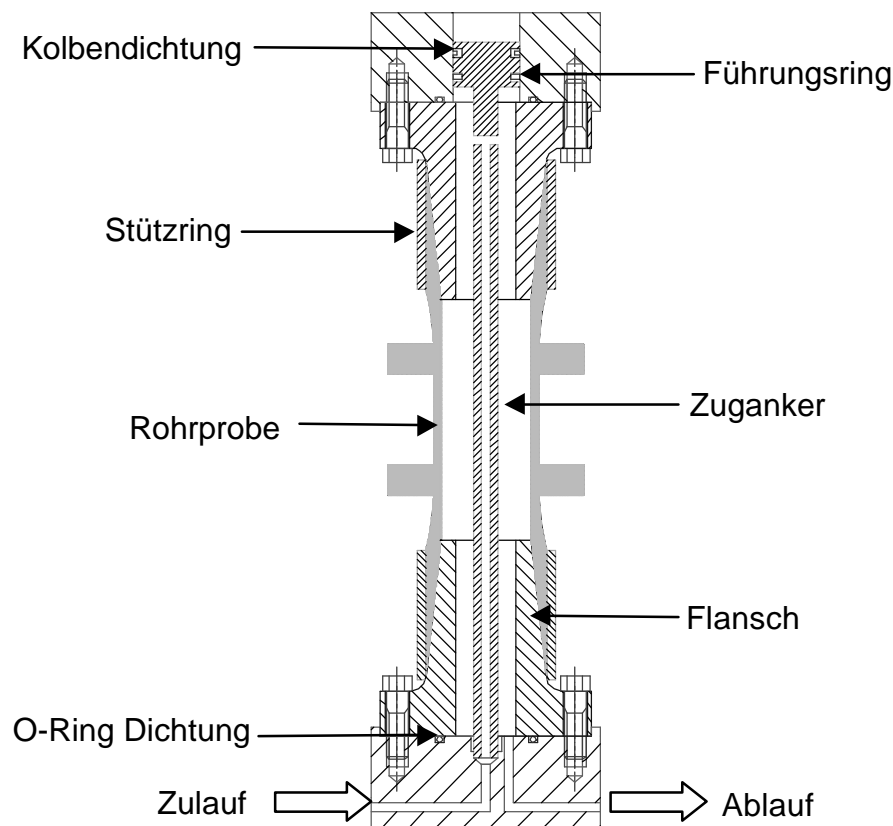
Flanschkonstruktion für Innendruckversuche mit Axialkraftausgleich
